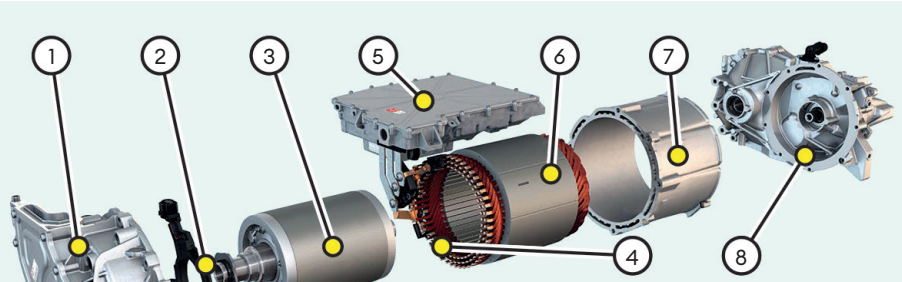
Die E-Maschine in der Explosionsdarstellung. 1 Getriebegehäuse, 2 Resolver (Lagesensor) - 3 Rotor - 4 Wicklungskopf - 5 Leistungselektronik - 6 Stator - 7 Motorgehäuse - 8 Zwischengehäuse
